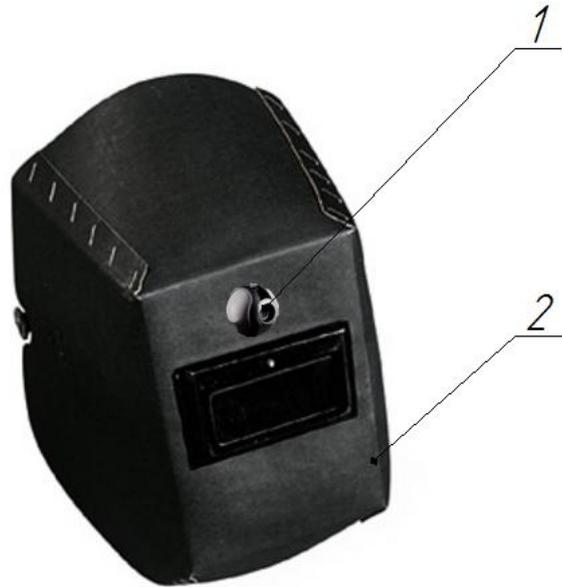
Сварочная маска с камерой: 1 – камера, 2 – сварочная маска
